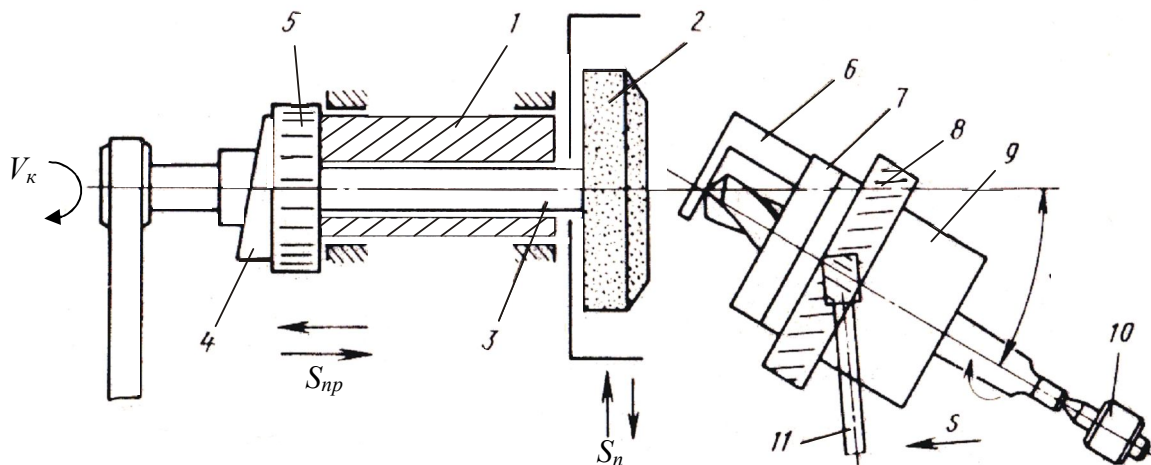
Схема заточування свердла по гвинтовій поверхні
